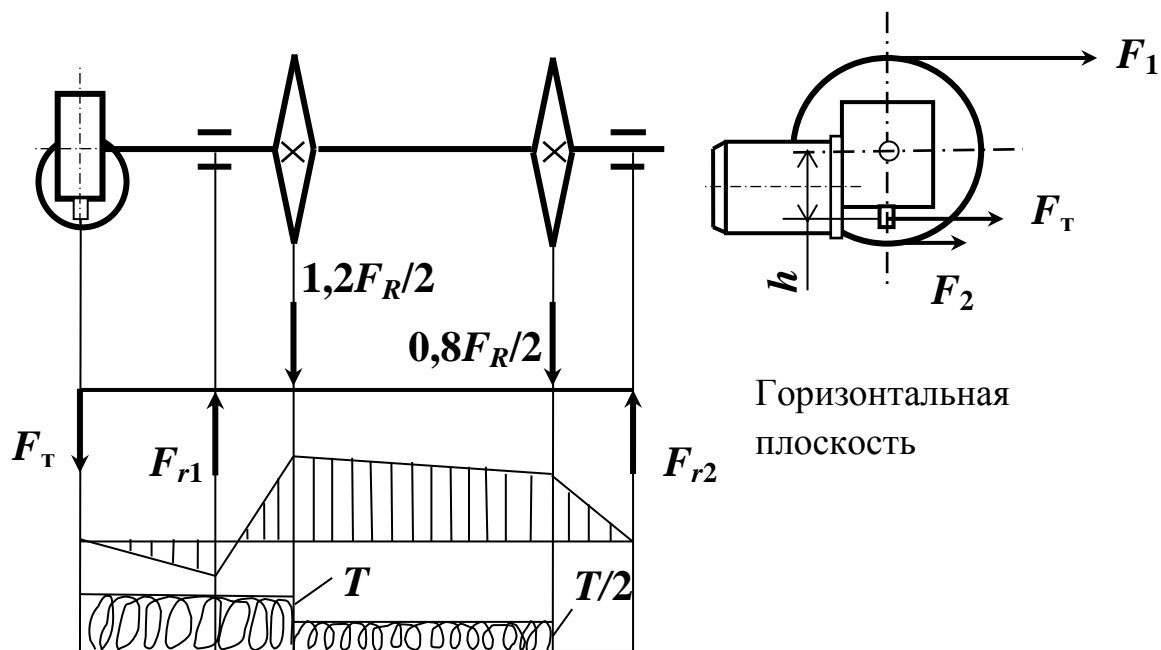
Вал с двумя тяговыми звездочками и навесным мотор-редуктором
